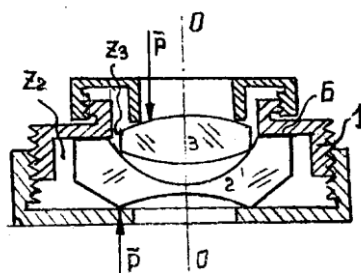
Базировка второй линзы на торец корпуса: 1- корпус; 2,3- линзы; Б – торец второй линзы, \bar{P} – усилие
